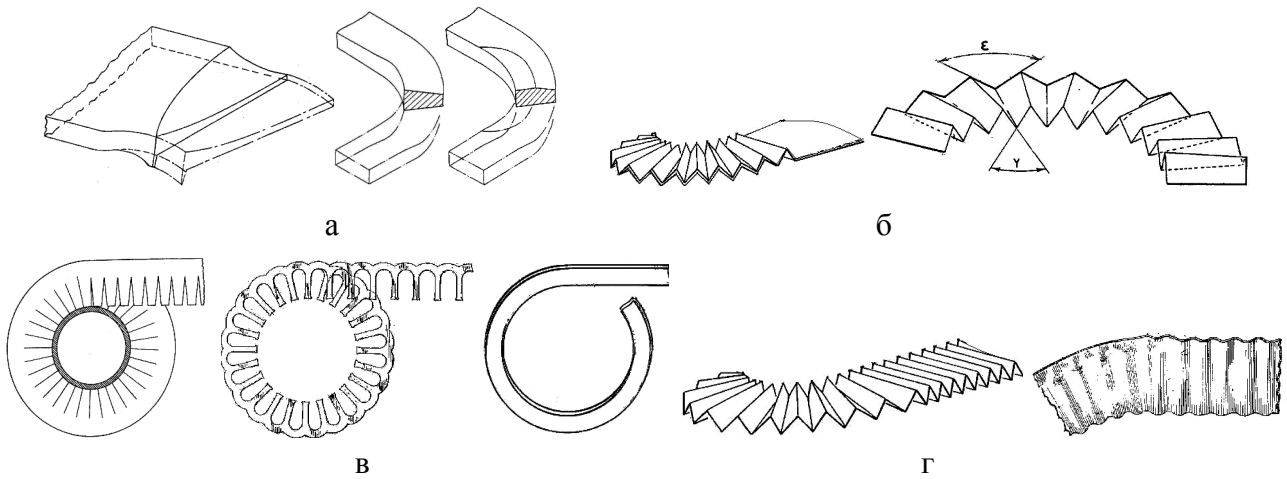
Схеми згину початкових заготовок у процесах формоутворення гвинтових заготовок:
